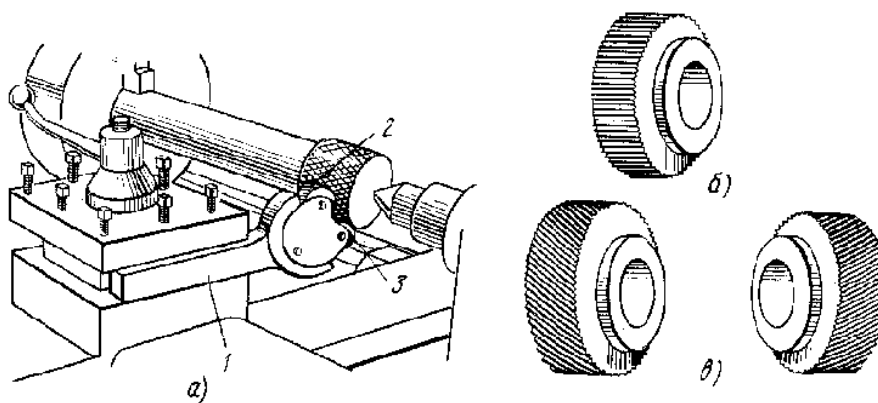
а) обкатка зубчатыми валиками, б) прямозубый валик, в) косоозубые валики
